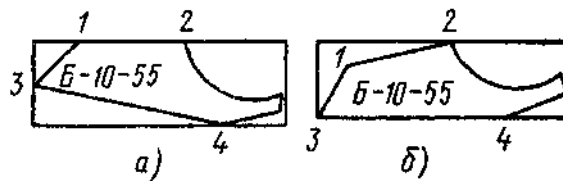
Побудова описаного прямокутника однієї і тієї ж заготовки деталі Б-10-55
